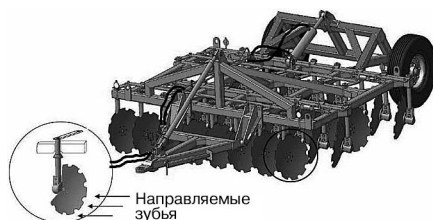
Объект управления – зубчатые диски почвообрабатывающего агрегата
